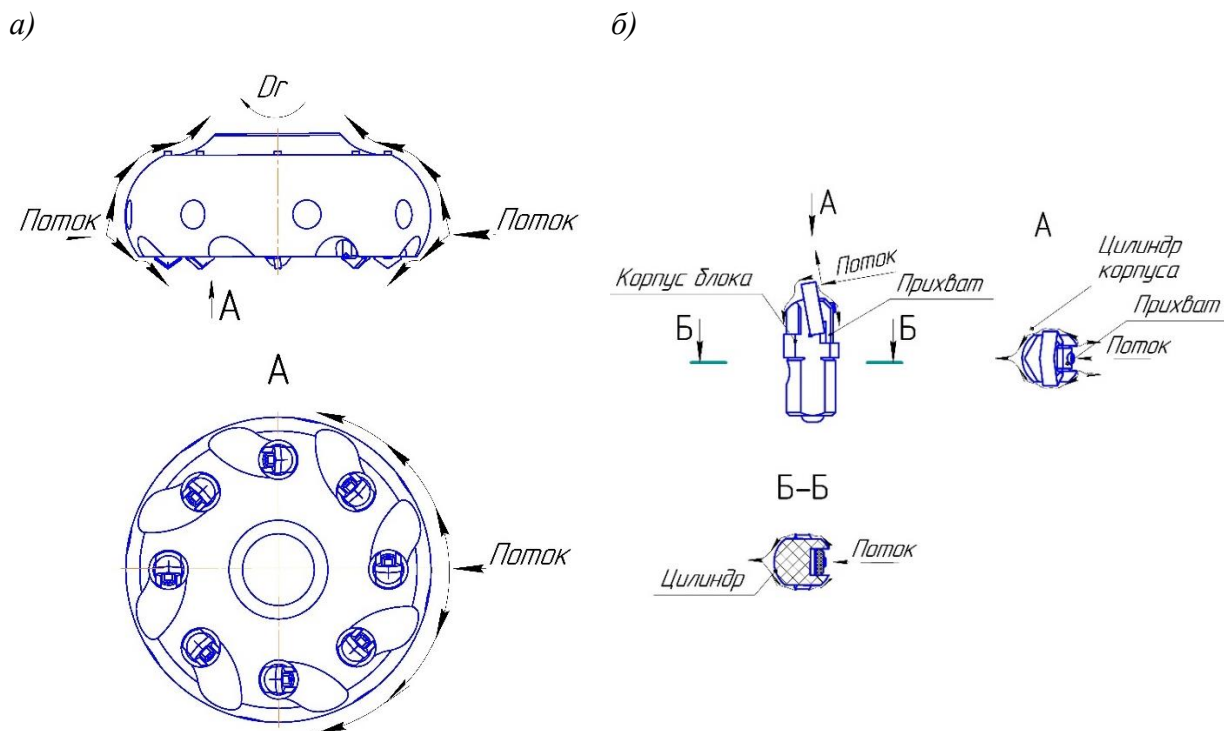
Схемы обтекания воздушными и жидкими потоками корпусов (а) и конструктивных элементов резцовых блоков (б)
